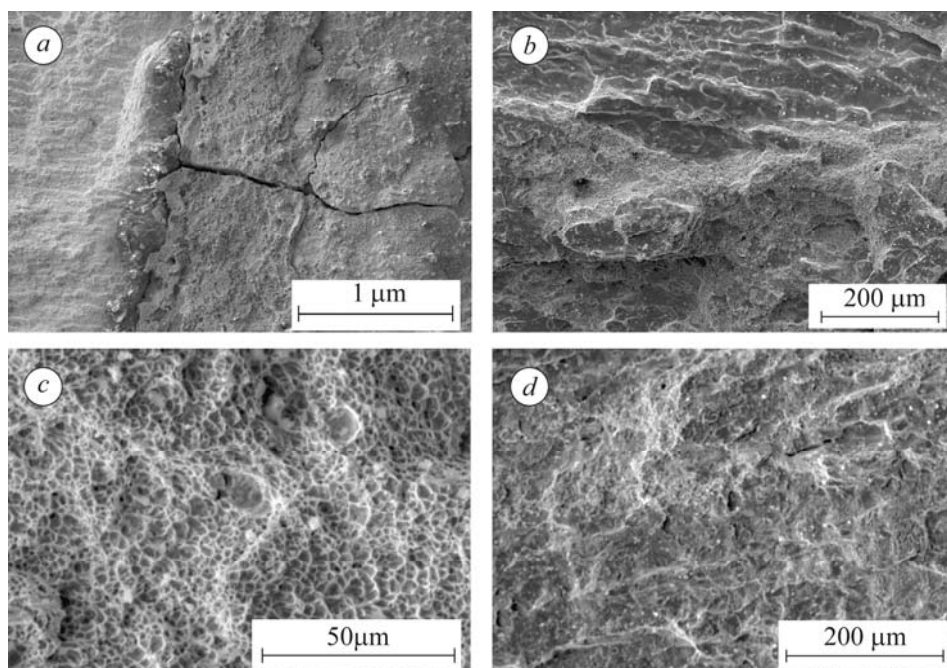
Мікромеханізми руйнування в зоні “зварний шов–основний метал” (a, b) та основного металу (c) і зварного шва (d).
